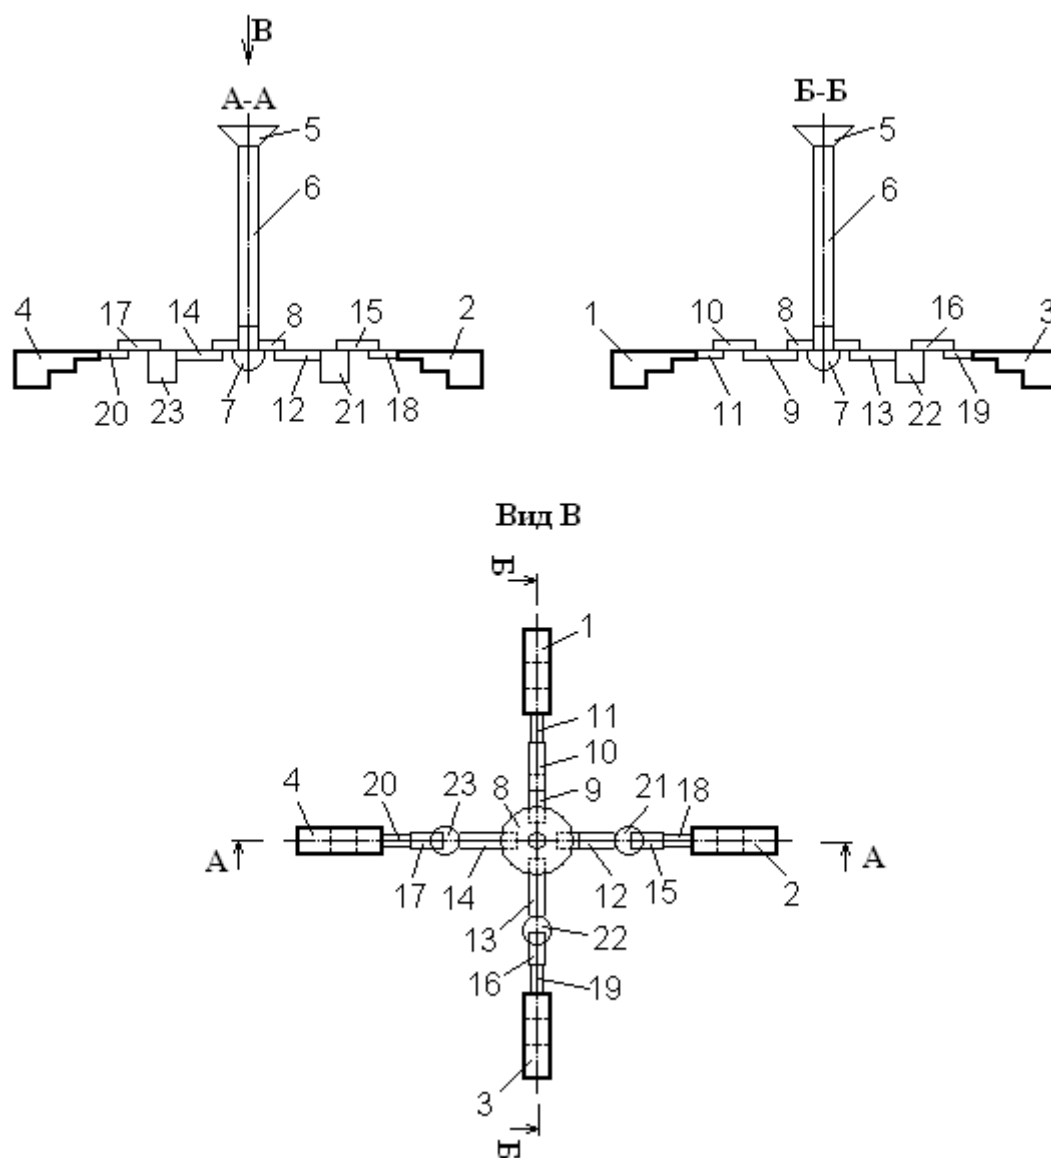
Схема литниковой системы для изготовления отливок с разной структурой и свойствами из одного базового расплава в общей литейной форме
